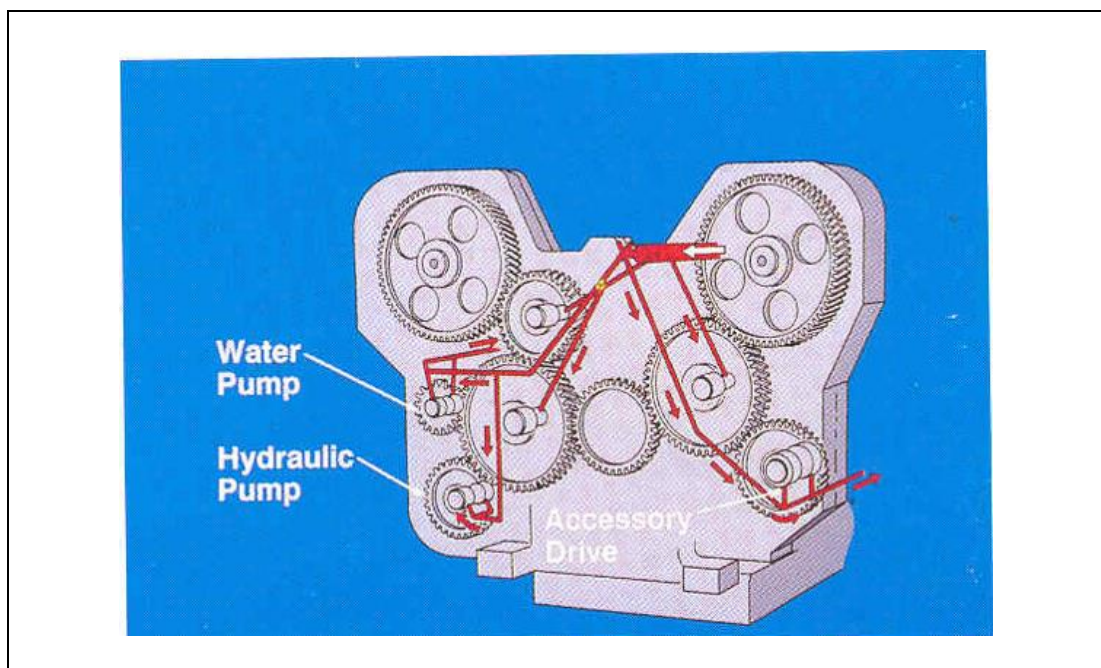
Carcasa frontal de engranes Motor Cummins K2000. (Cummins, 2004)
